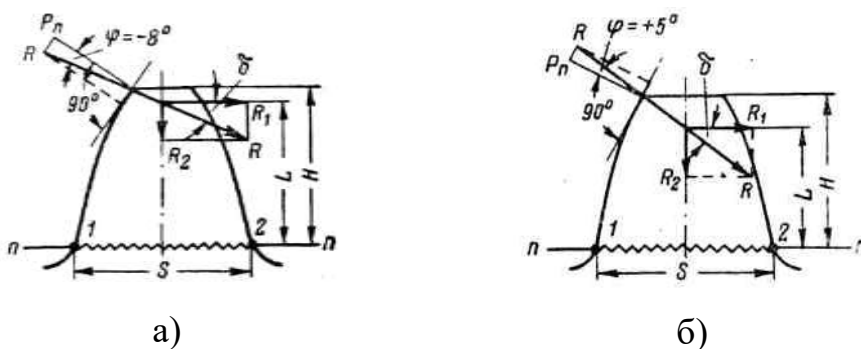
Схема сил, що діють на зуб шестерні (а), та зуб зубчатого колеса (б) з урахуванням сил тертя
